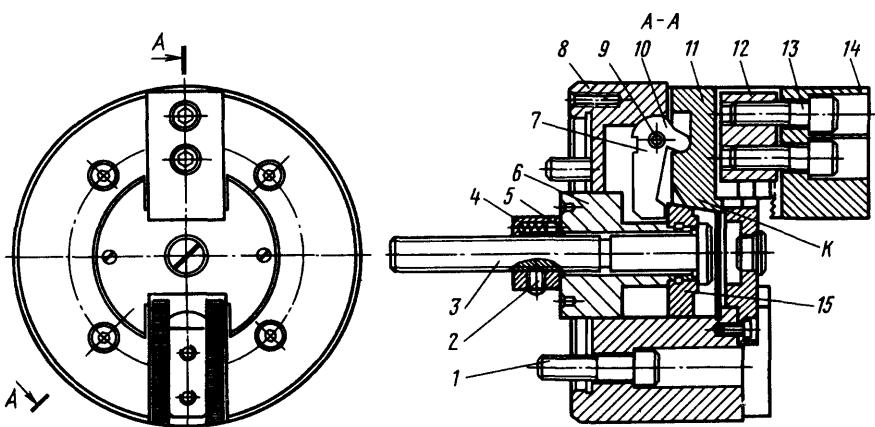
Двухкулачковый рычажный патрон со сменными кулачками
